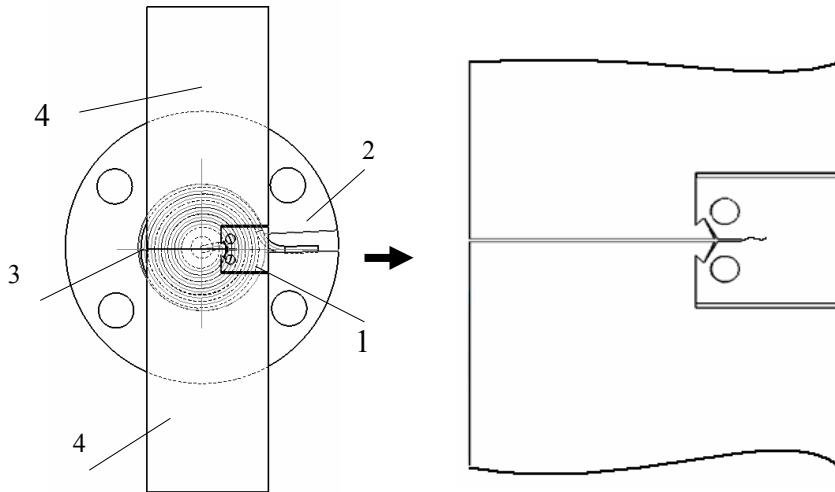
Розташування СТ зразка при обробці: 1 – зразок; 2 – корпус індуктора; 3 – витки індуктора, 4 – тяги для механічного навантаження
